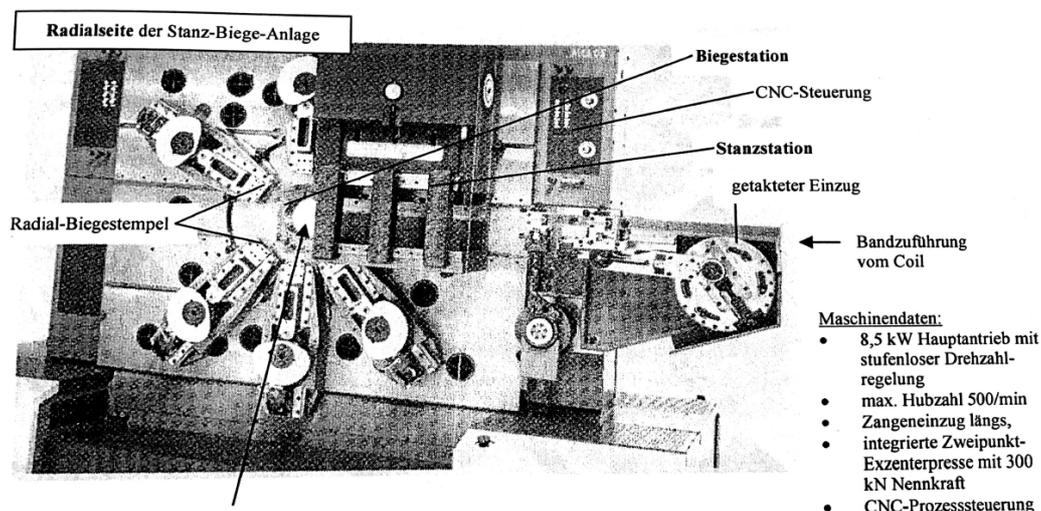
Aufbau einer Biegemaschine(Schwenkbiegen) [1]
